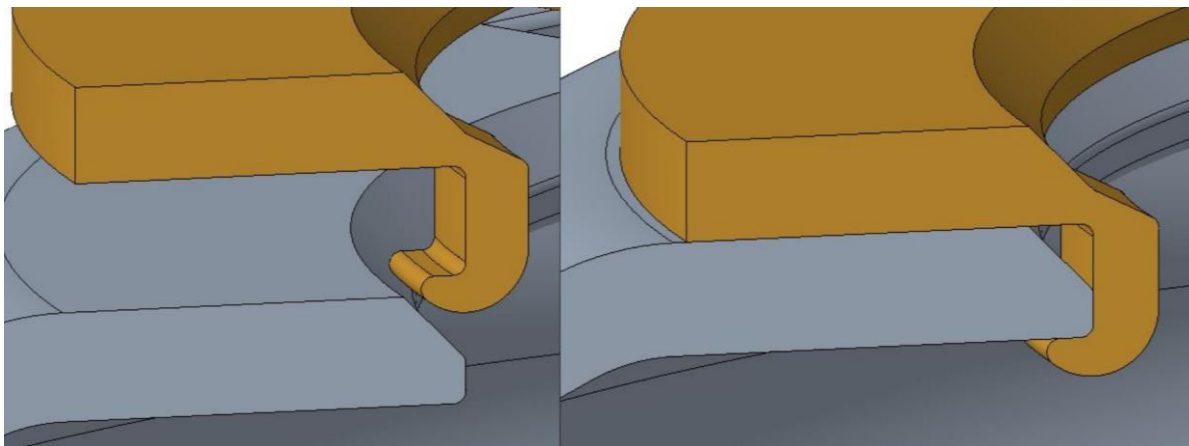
Detail spojení podložky s vnějším kroužkem ložiska
